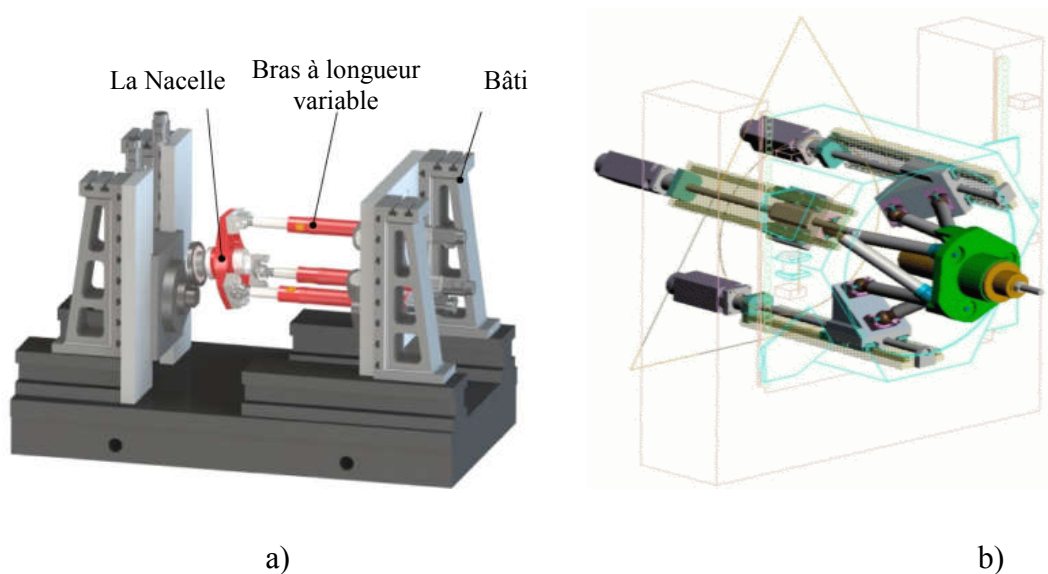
a) Prototype Virtual d'une machine-outil a bras variable. b) machine-outil à structure parallèle bras fixe [47].
